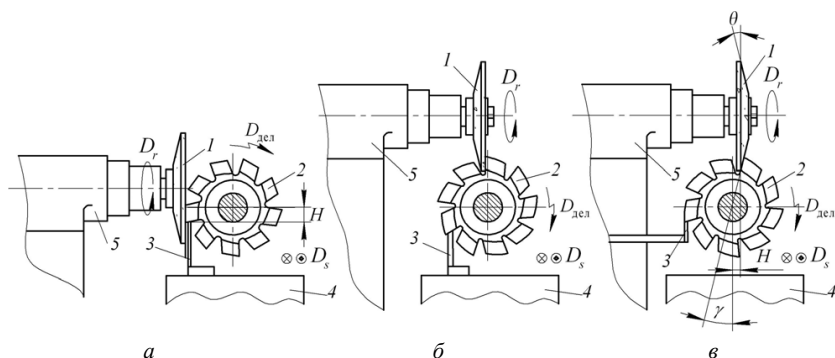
Схемы заточки фрез по задней (а) и передней (б, в) поверхностям: 1 – шлифовальный круг; 2 – фреза; 3 – упорка; 4 – стол станка; 5 – шлифовальная головка
